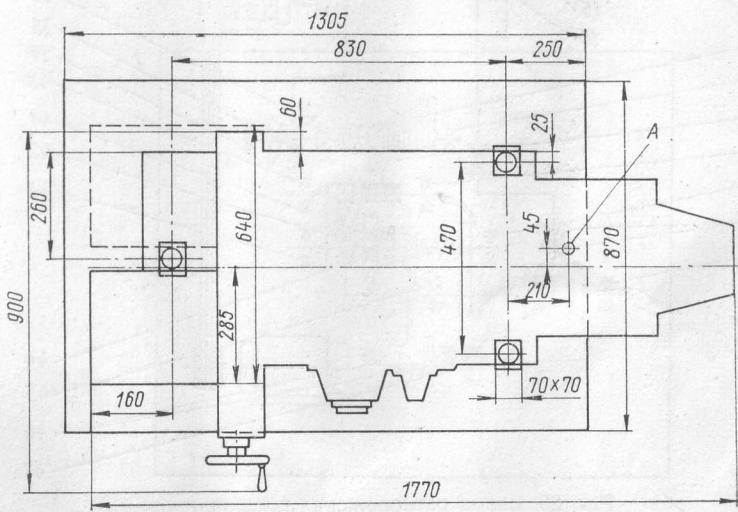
Габаритные размеры и план фундамента станка 7А33:
